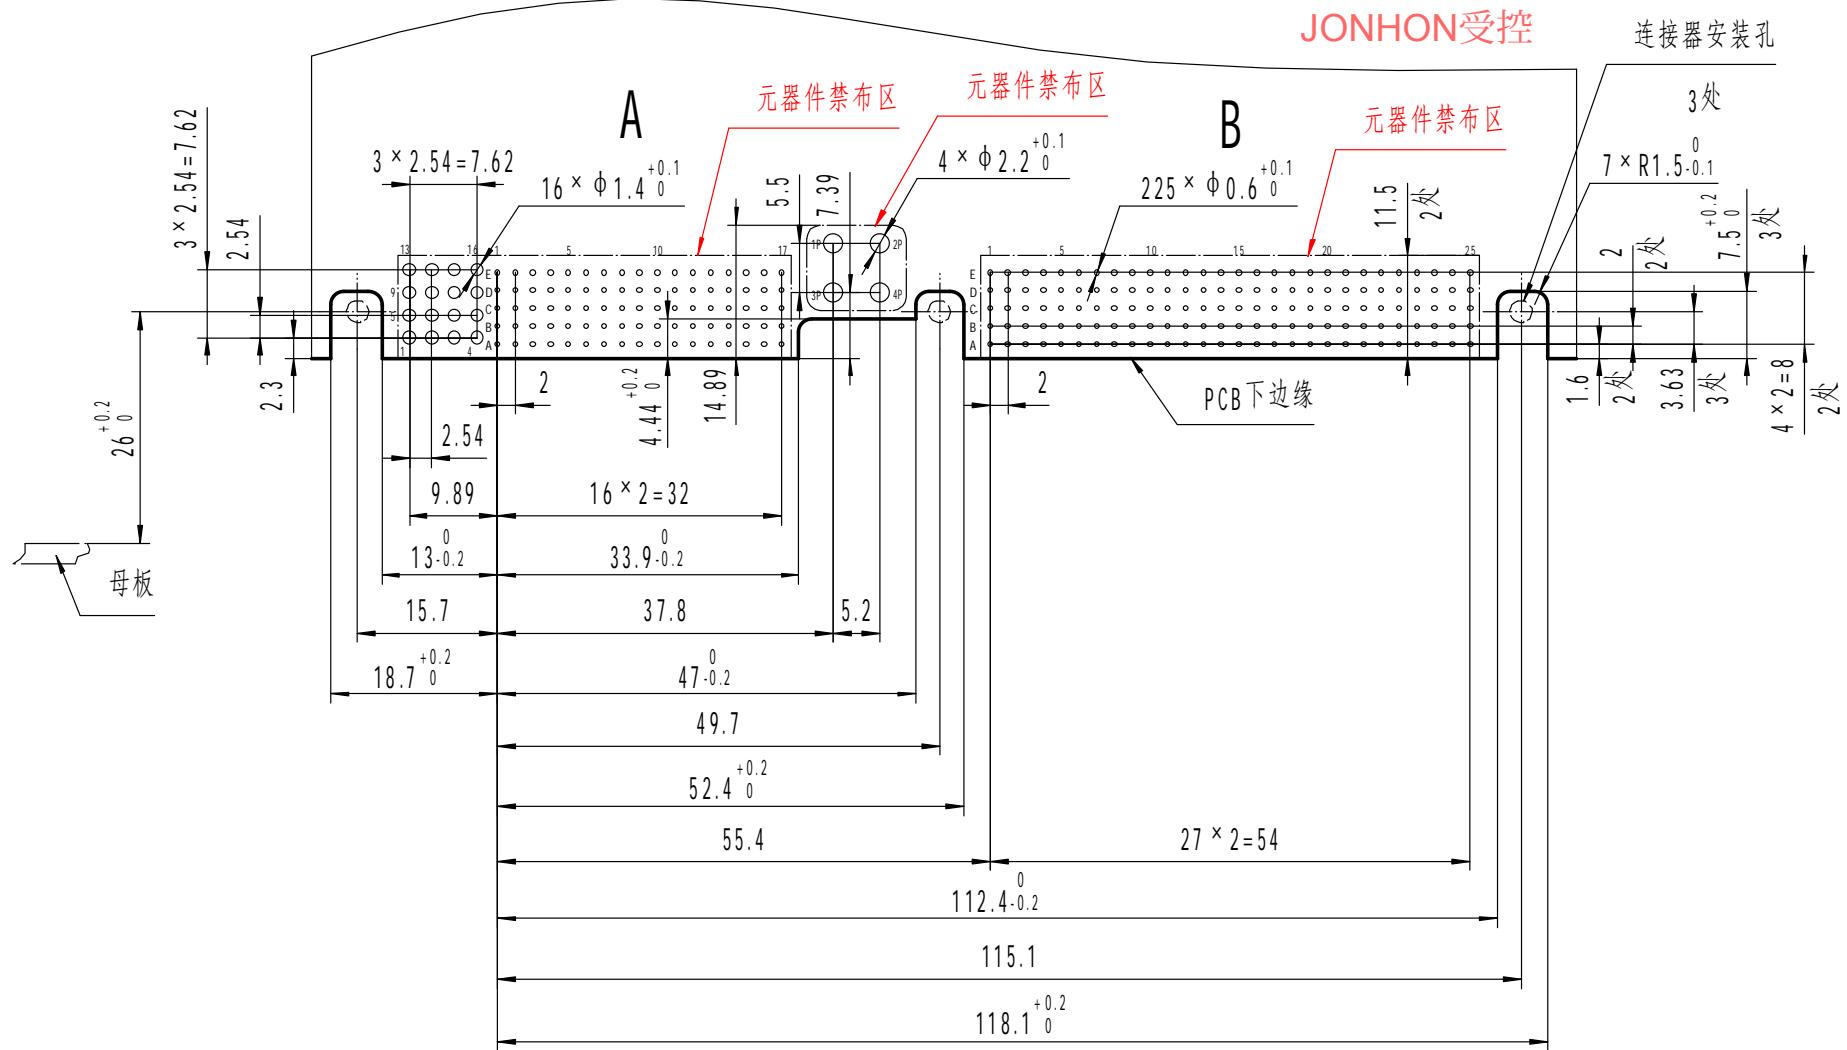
LRM1-A85H16BH4RB-B140-T※推荐 PCB 开孔尺寸图 (未注公差按±0.02mm) (图 2 中 N 向视图)
